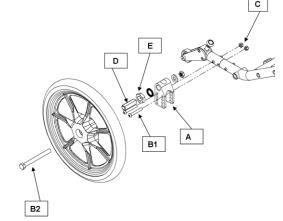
Installation de la roue arrière de 16 po (40,6 cm)
